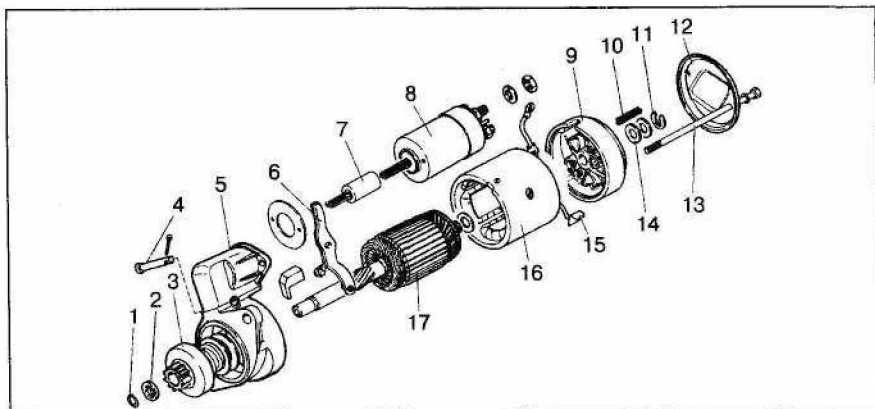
Детали стартера 39.3708: 1 — стопорное кольцо; 2 — ограничительное кольцо; 3 — привод; 4 — ось рычага; 5 — передняя крышка; 6 — рычаг привода; 7 — якорь тягового реле; 8 — тяговое реле; 9 — задняя крышка; 10 — пружина щетки; 11 — стопорная шайба; 12 — кожух; 13 — стяжной болт; 14 — регулировочные шайбы; 15 — щетка; 16 — корпус; 17 — якорь
